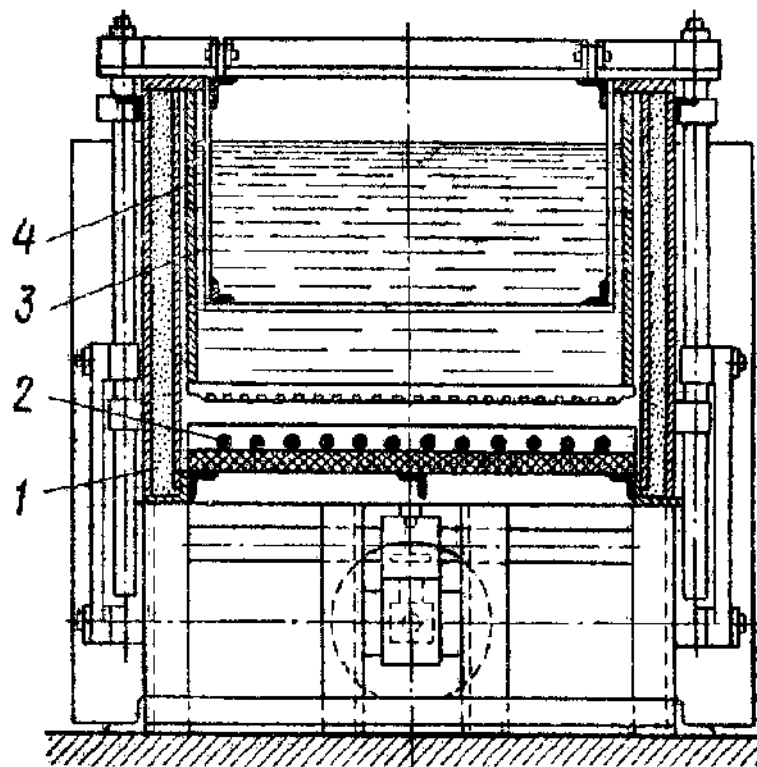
Схема масляной ванны для нагрева подшипников:
